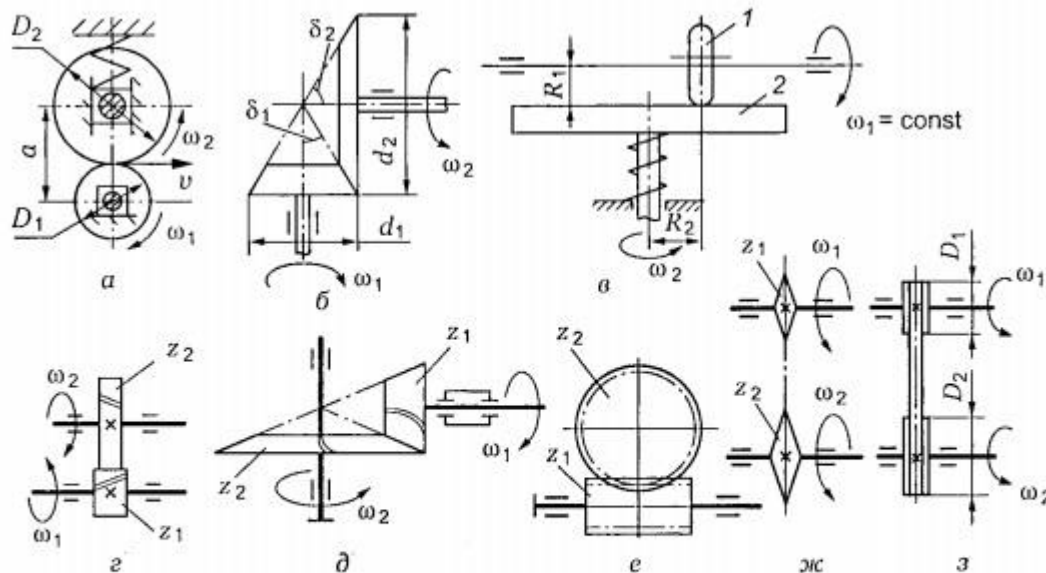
Кинематические схемы механических передач: а — цилиндрическая фрикционная передача; б — коническая фрикционная передача; в — фрикционный вариатор: 1 — ролик; 2 — ведомый диск; г — цилиндрическая зубчатая передача; д — коническая зубчатая передача; е — червячная передача; ж — цепная передача; з — ременная передача
